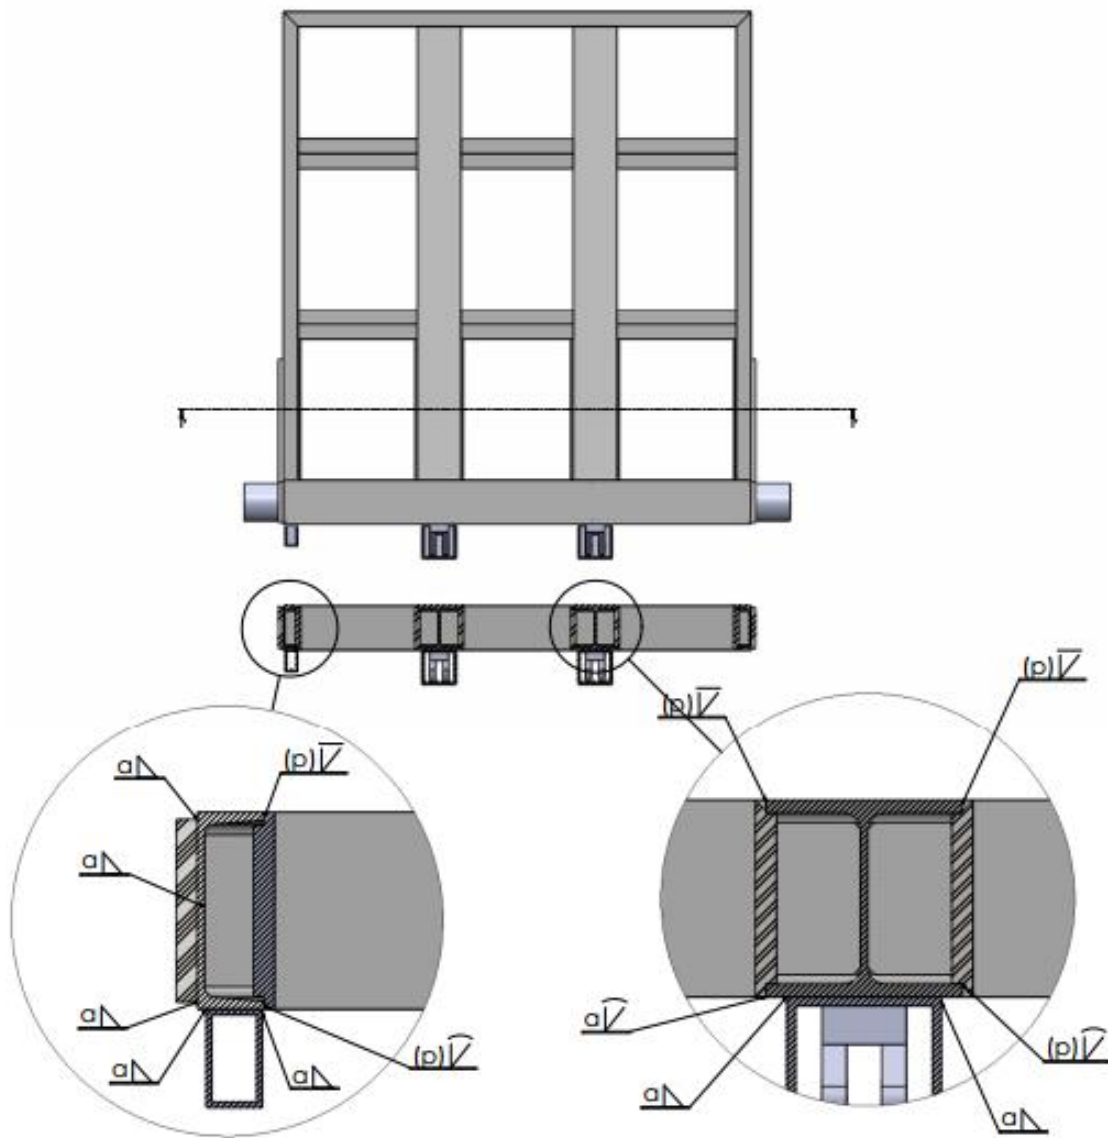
Simbologia para soldadura dos componentes de reforço do suporte em "L".
